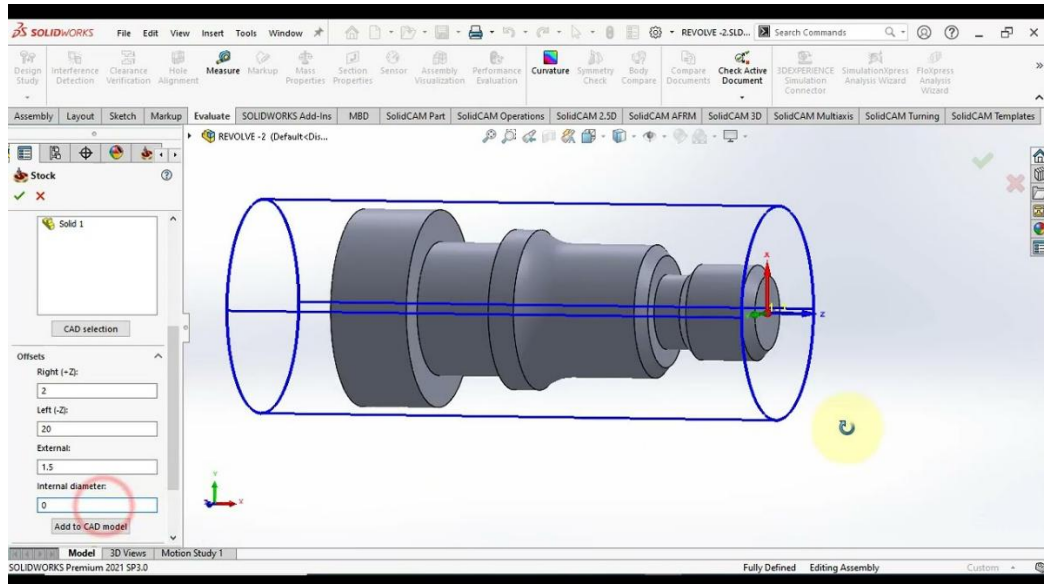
Установ 1 — токарна та свердлильна обробка
